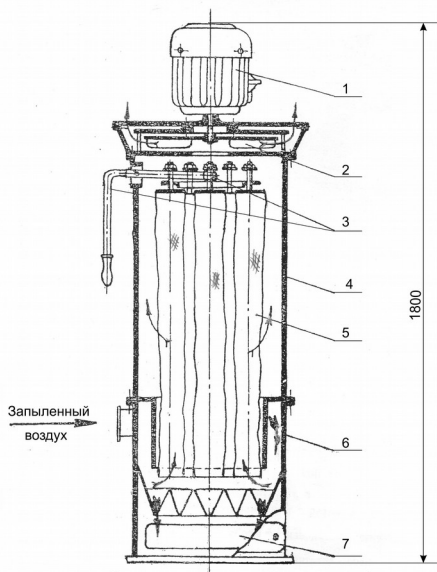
Пылеулавливающий агрегат ЗИЛ-800:
